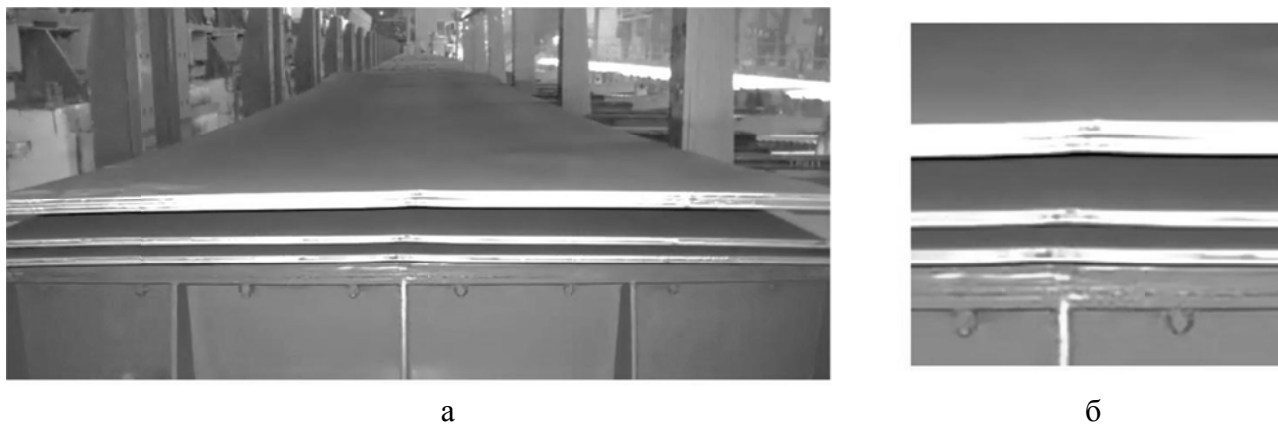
Вид торцевой поверхности листов, порезанных шевронными ножами:
